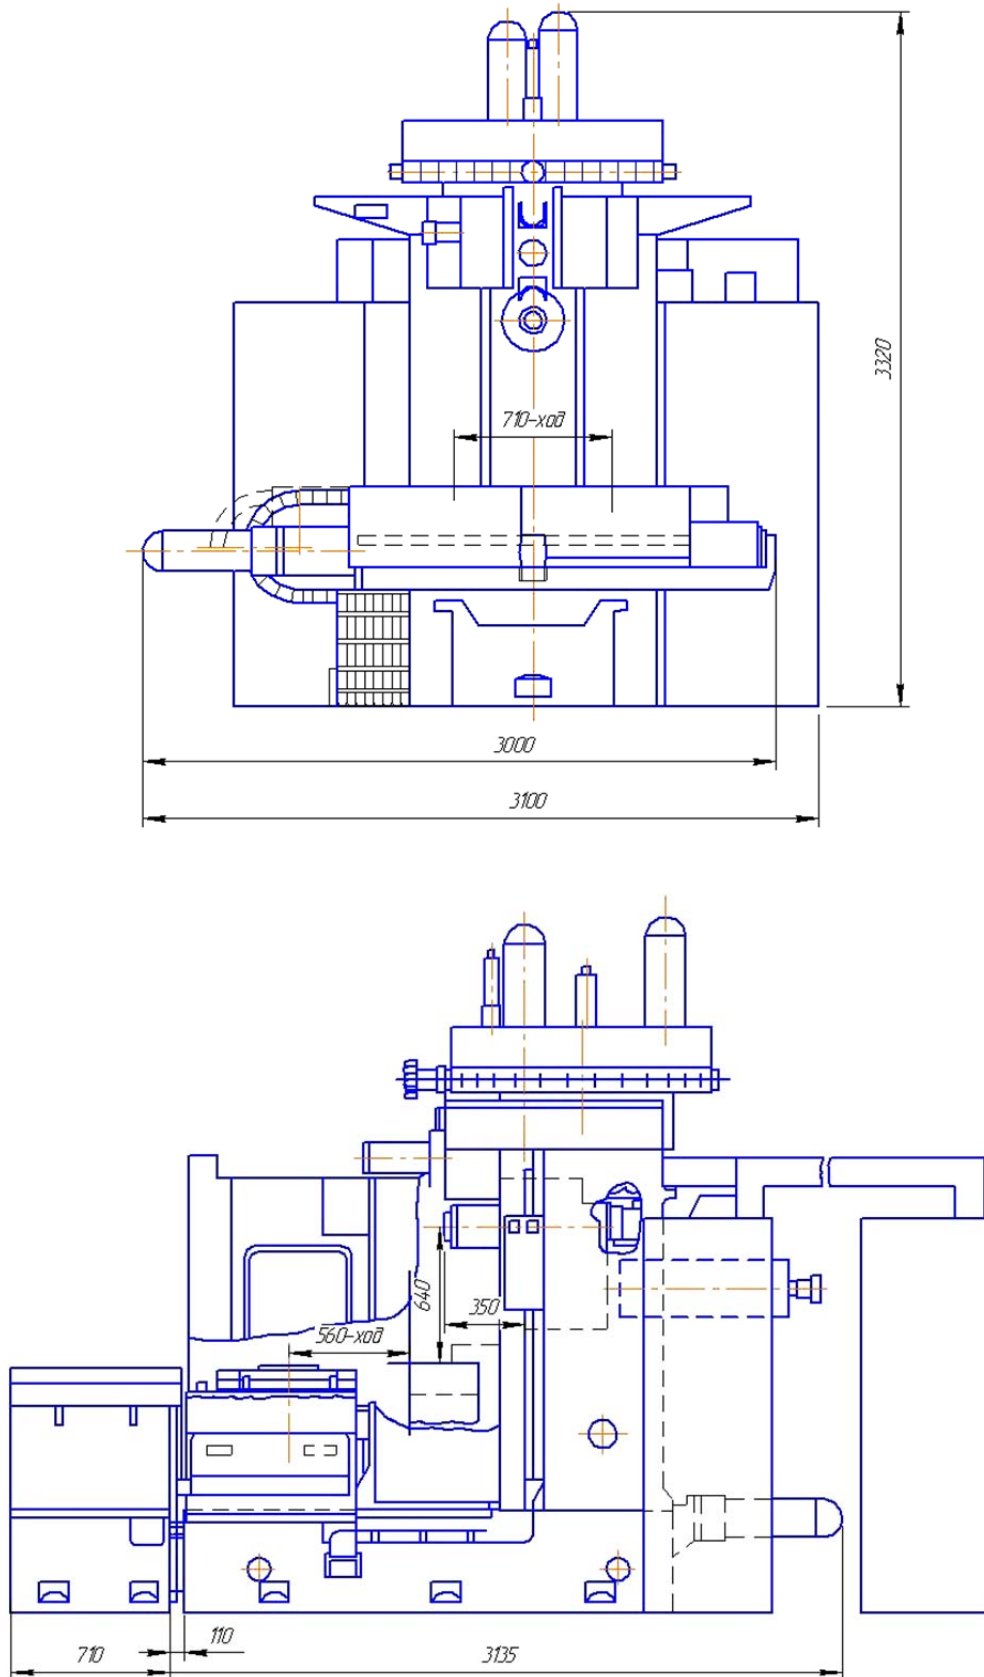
Общий вид обрабатывающего центра ОЦЗВ
